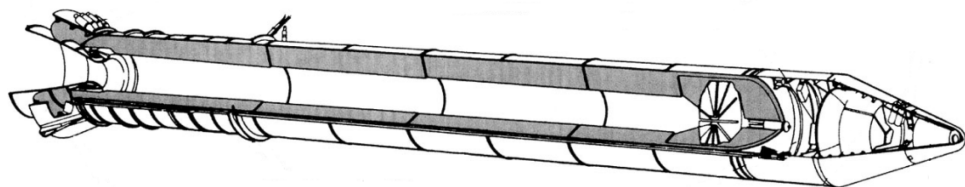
Твердотопливный ракетный ускоритель Space Shuttle
